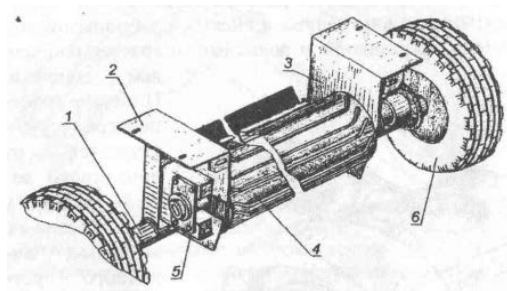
Основание камеры: 1 – ось; 2 и 3 – боковины; 4 – валец нижний задний; 5 – корпус подшипника; 6 – колесо
